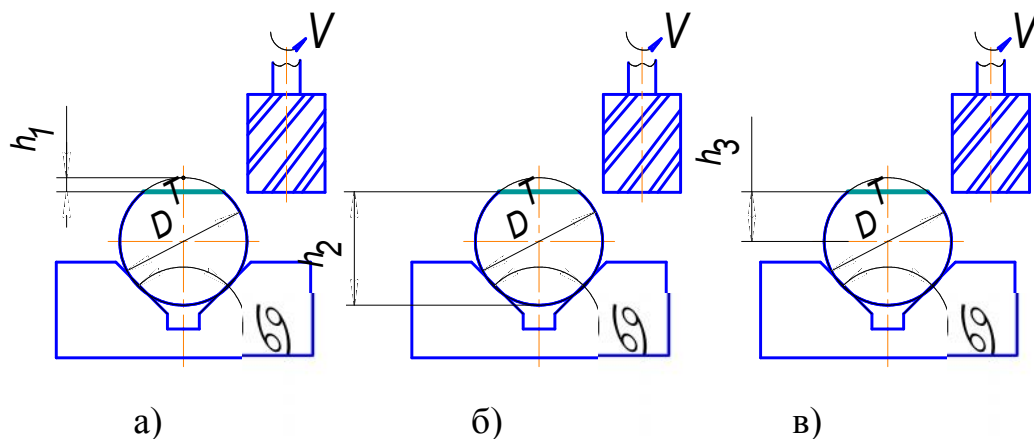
Варианты простановки размеров до обрабатываемой поверхности заготовки, установленной в призму
